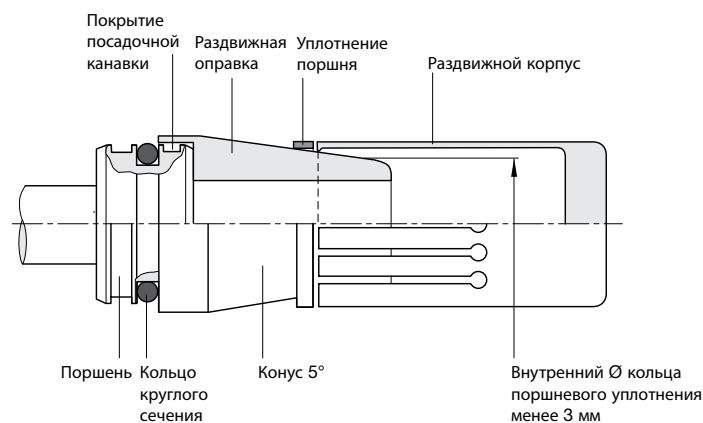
Slipper Seal®поршневого типа, установка, шаг 3. Комплект растягивающих инструментов для установки уплотнения Slipper Seal®поршневого типа.
